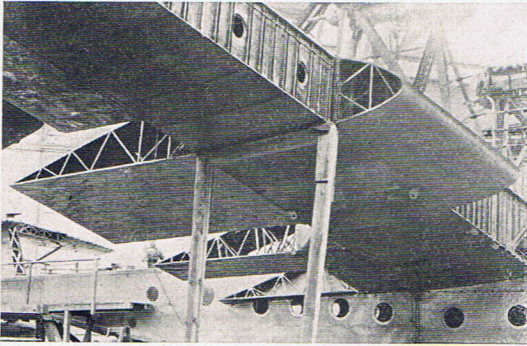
Caisson central d'aile avec caissons de profilage appliqués
